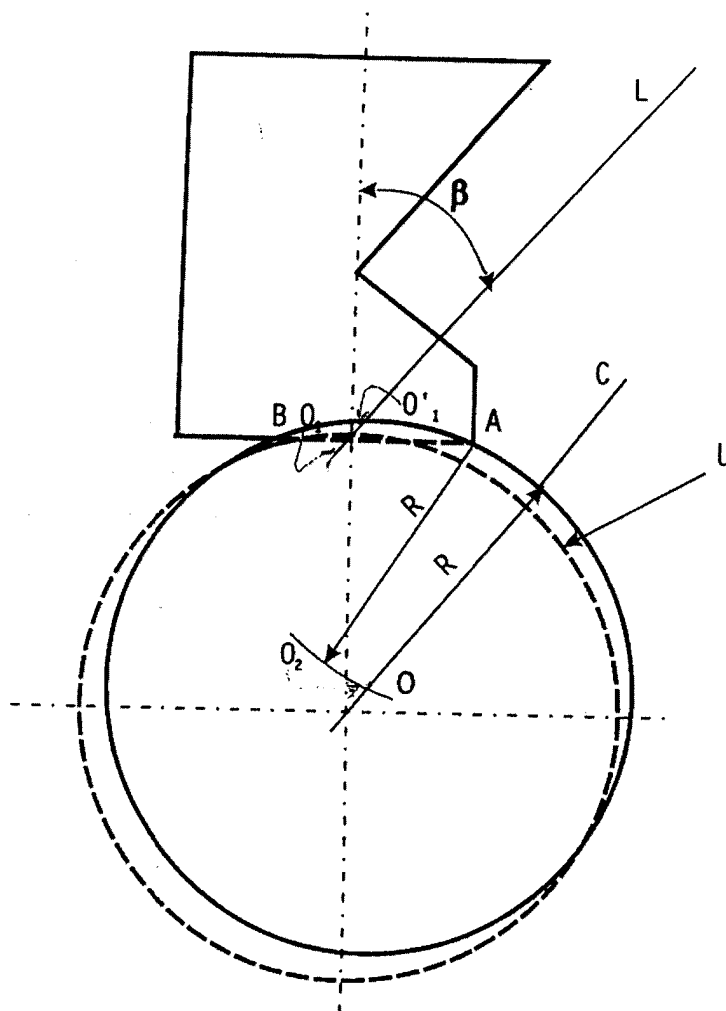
Разметка призмы преобразователя для сопряжения с изделием
